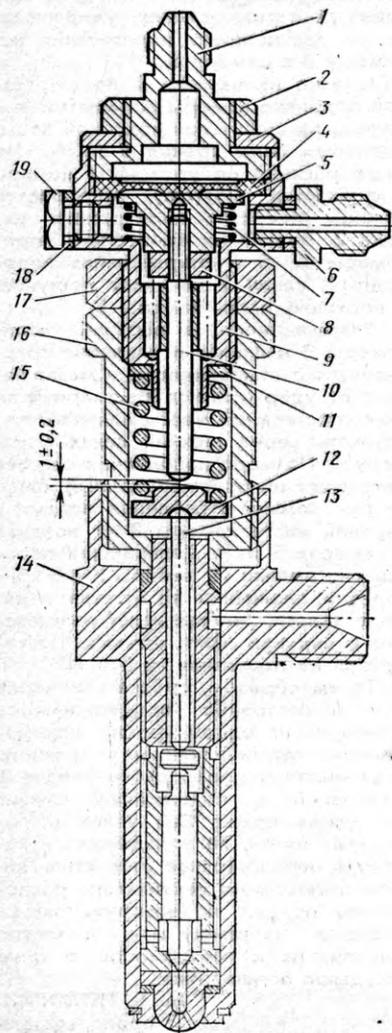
Приставка-догрузатель в сборе с форсункой: 1 — крышка-штуцер; 2 — контргайка; 3 — шайба; 4 — мембрана; 5 — опора; 6 — штуцер для слива топлива; 7 — возвратная пружина; 8 — контргайка; 9 — корпус; 10 — толкатель; 11 — регулировочная шайба; 12 — опора (тарелка) пружины (форсунки); 13 — толкатель форсунки; 14 — корпус форсунки; 15 — пружина форсунки; 16 — нажимной стакан форсунки; 17 — контргайка форсунки; 18 — медные прокладки; 19 — заглушка
